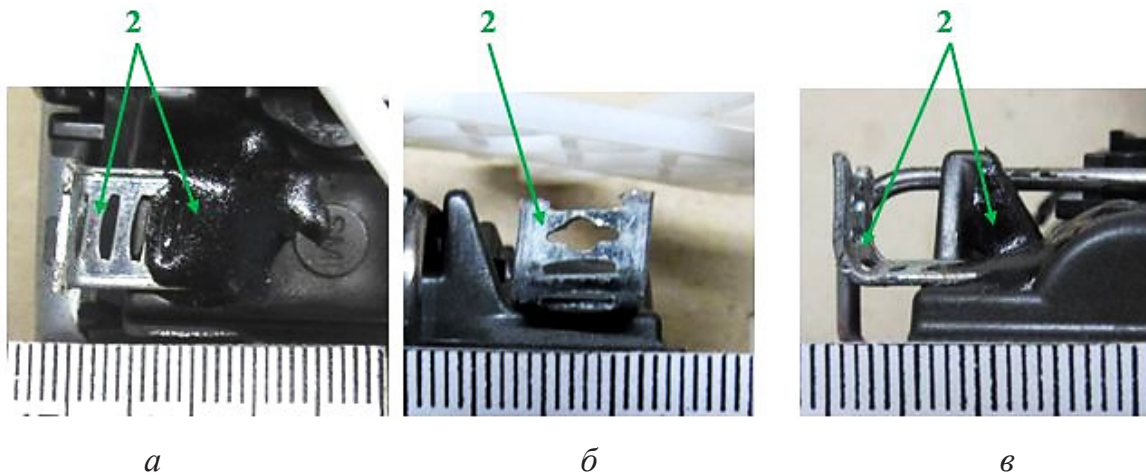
Загальний вигляд металевої пластини з нашаруванням полімерної речовини чорного кольору: *а* – вигляд зверху; *б* – вигляд збоку; *в* – вигляд збоку
